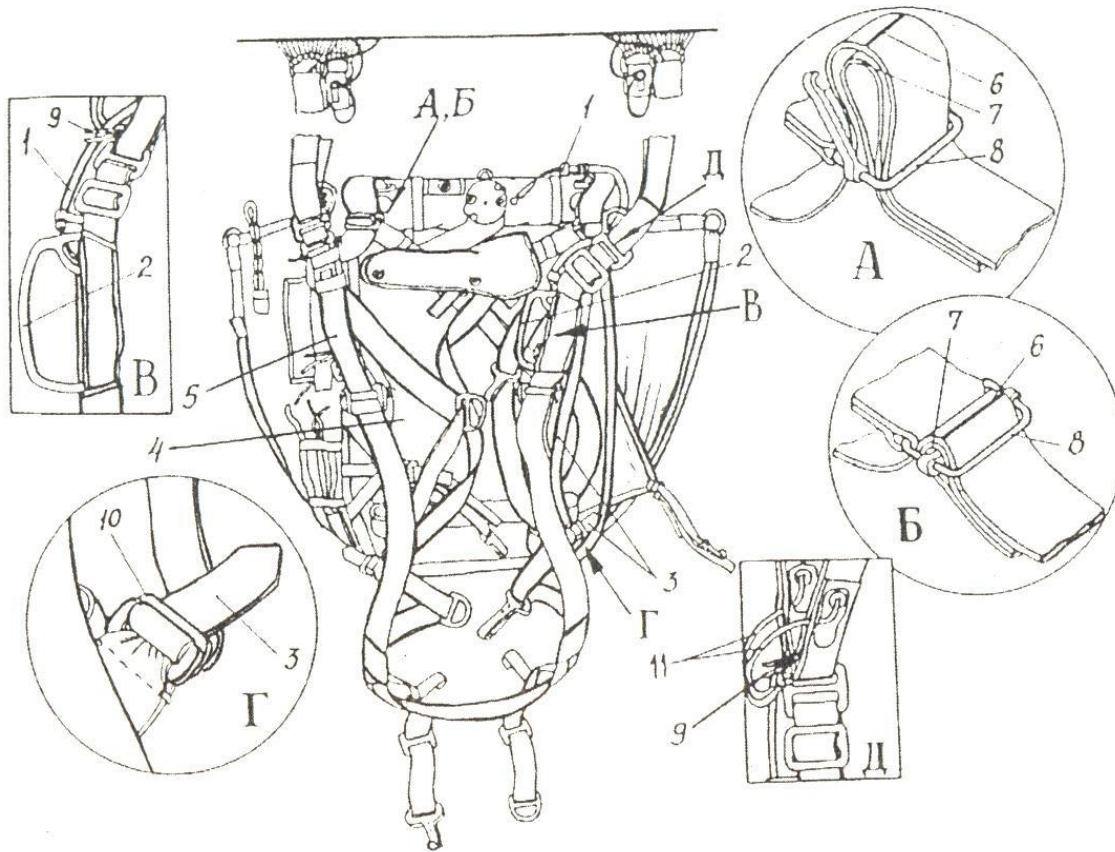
Монтаж звена ручного раскрытия, подсоединение к наспинно-плечевым обхватам пряжек с зубцами, монтаж регулирующих лент и укладка шариков в кармашки:
